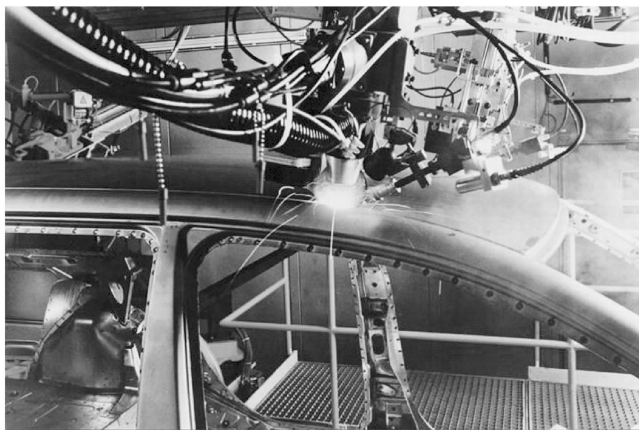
上海大众汽车公司的汽车车身焊接
